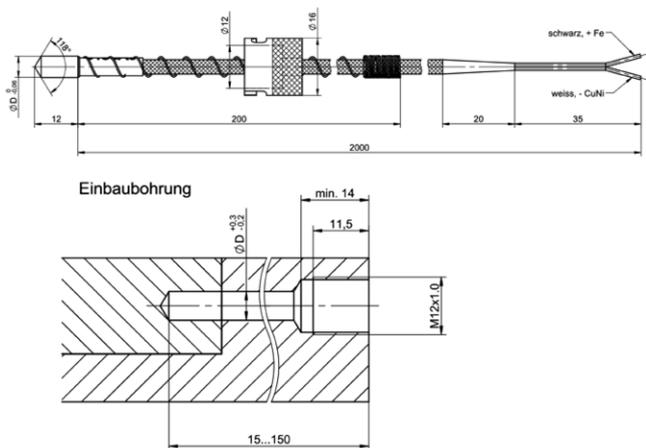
Einbau Typ 6198A... mit Bajonettverschluss
